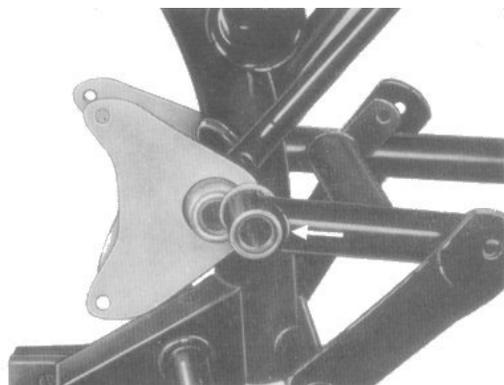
Druckring entfernt, Hinterradschwinge mit Anlaufscheiben in Pfeilrichtung bis Mitte Bohrung aufschieben
